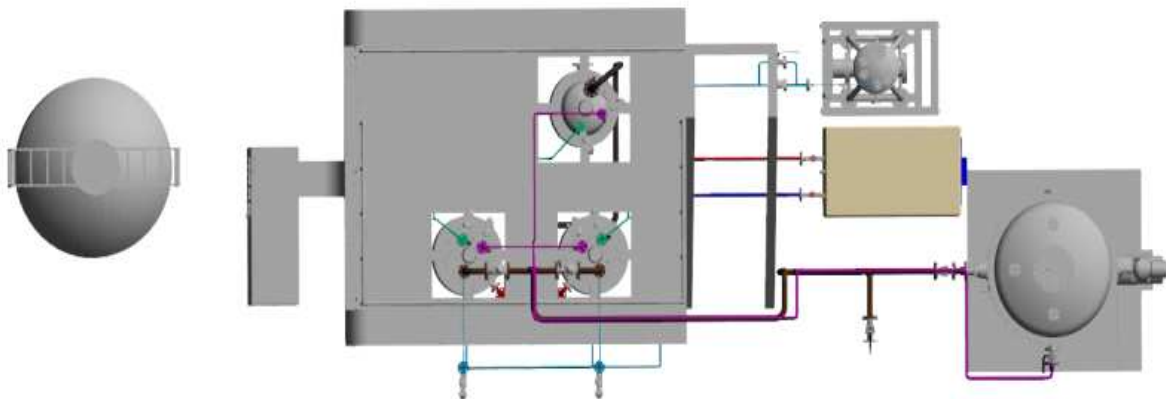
Pilot plant급 수열탄화 시스템3D 설계, 평면도
